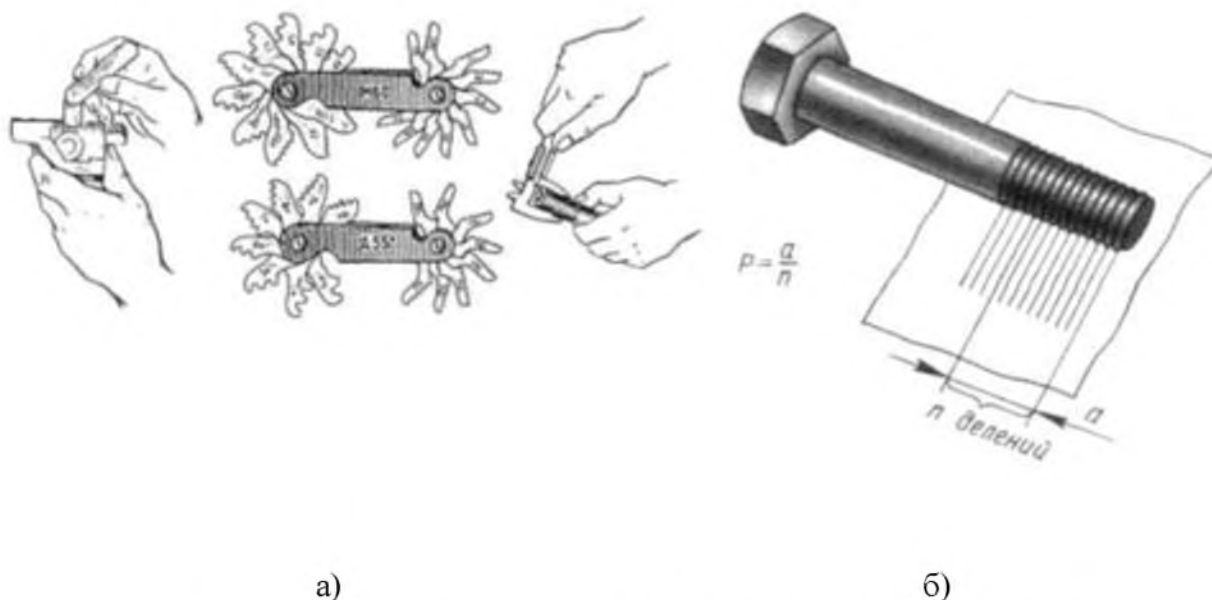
Измерение шага резьбы: а) резьбомером; б) линейкой
